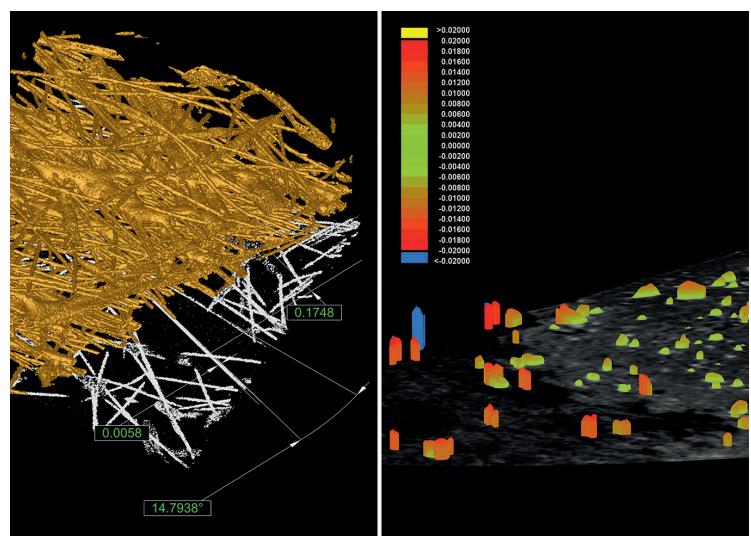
Faserstruktur eines Filters (links) und Eindringtiefe von Partikeln (rechts, Blick aus dem Werkstückinneren auf die Oberfläche) mit Dimensionen im einstelligen Mikrometerbereich © Werth Messtechnik
